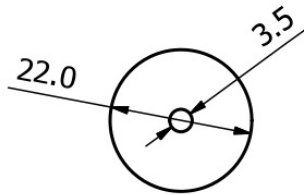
Dimensiones engrane acoplado al servomotor. Medidas en [mm].
